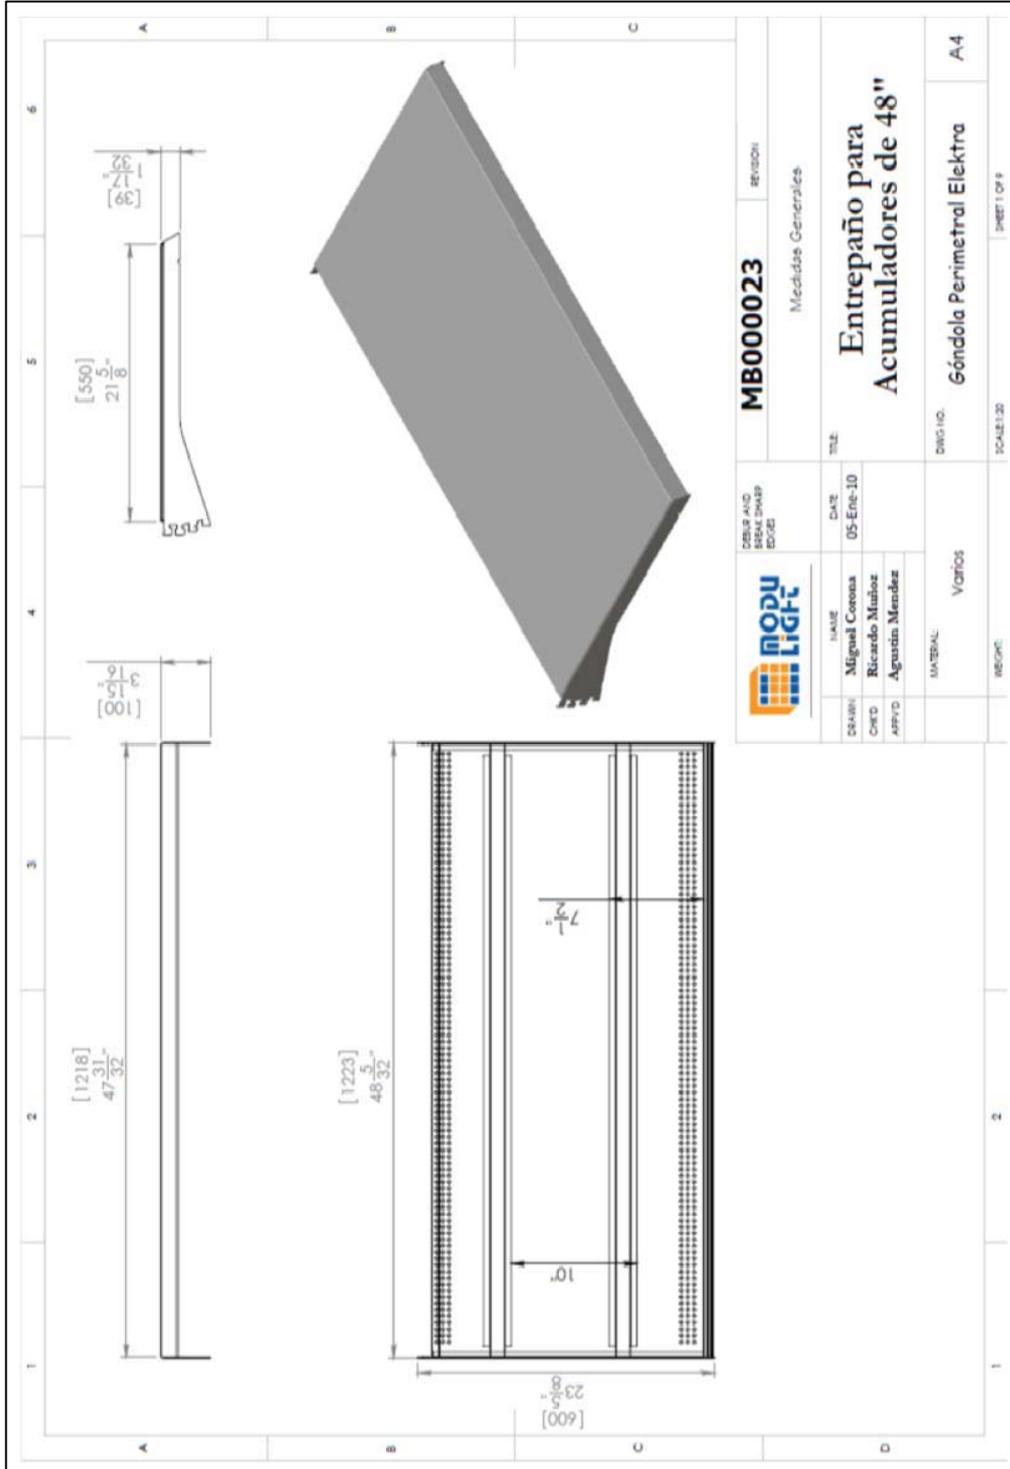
PLANO DE FABRICACIÓN DE ENTREPÁÑO CON MEDIDAS GENERALES
